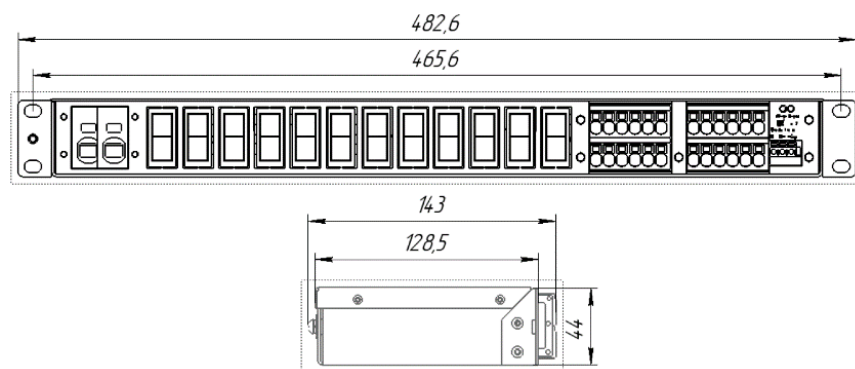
Габаритный чертеж ЩРЗ-9-1П
